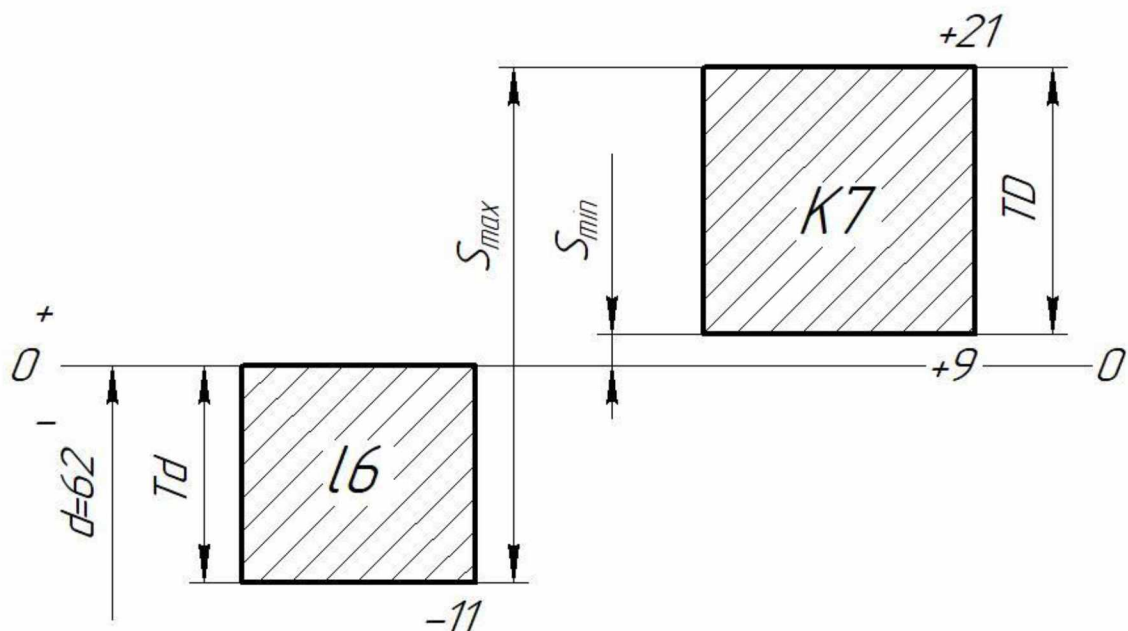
Схема полів допусків з'єднання з підшипником
